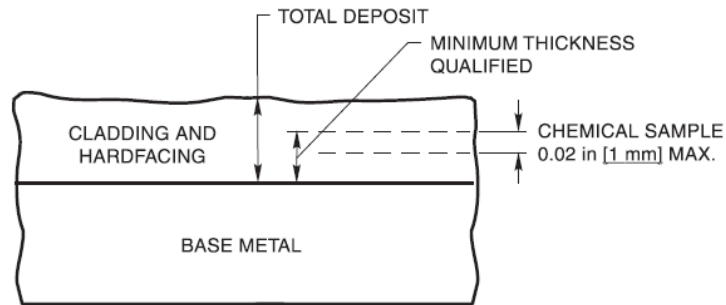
Muestra para análisis químico del revestimiento de soldadura (American Welding Society, 2009).
